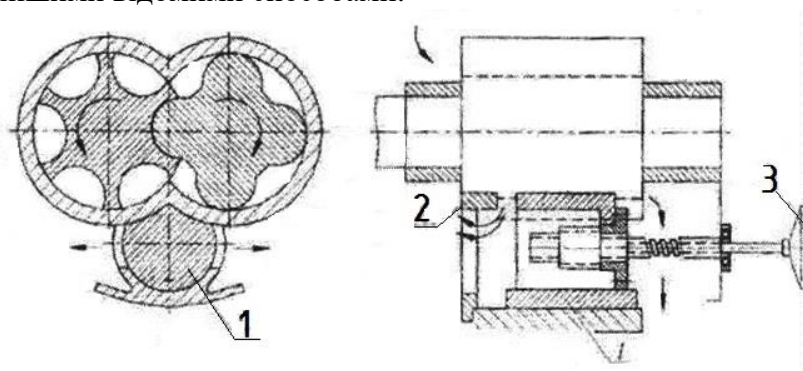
Гвинтовий компресор із золотниковим регулюванням: 1 – золотник; 2 – стопор; 3 – механізм привода
